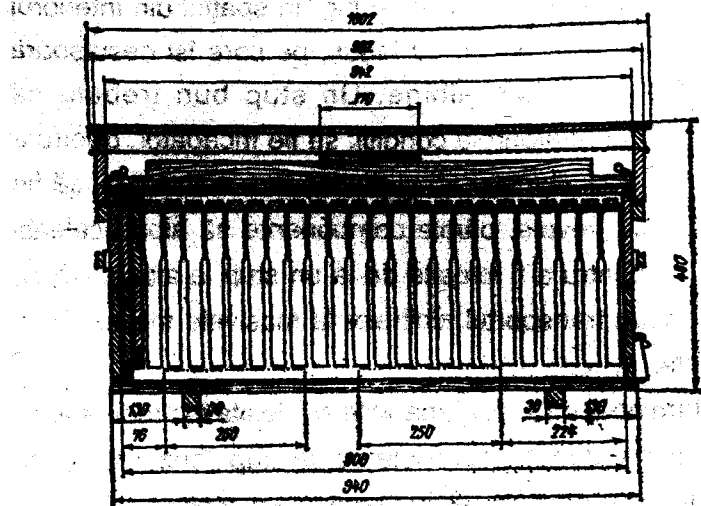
Secțiune transversală în stupul orizontal (STAS 4170 - 62)
